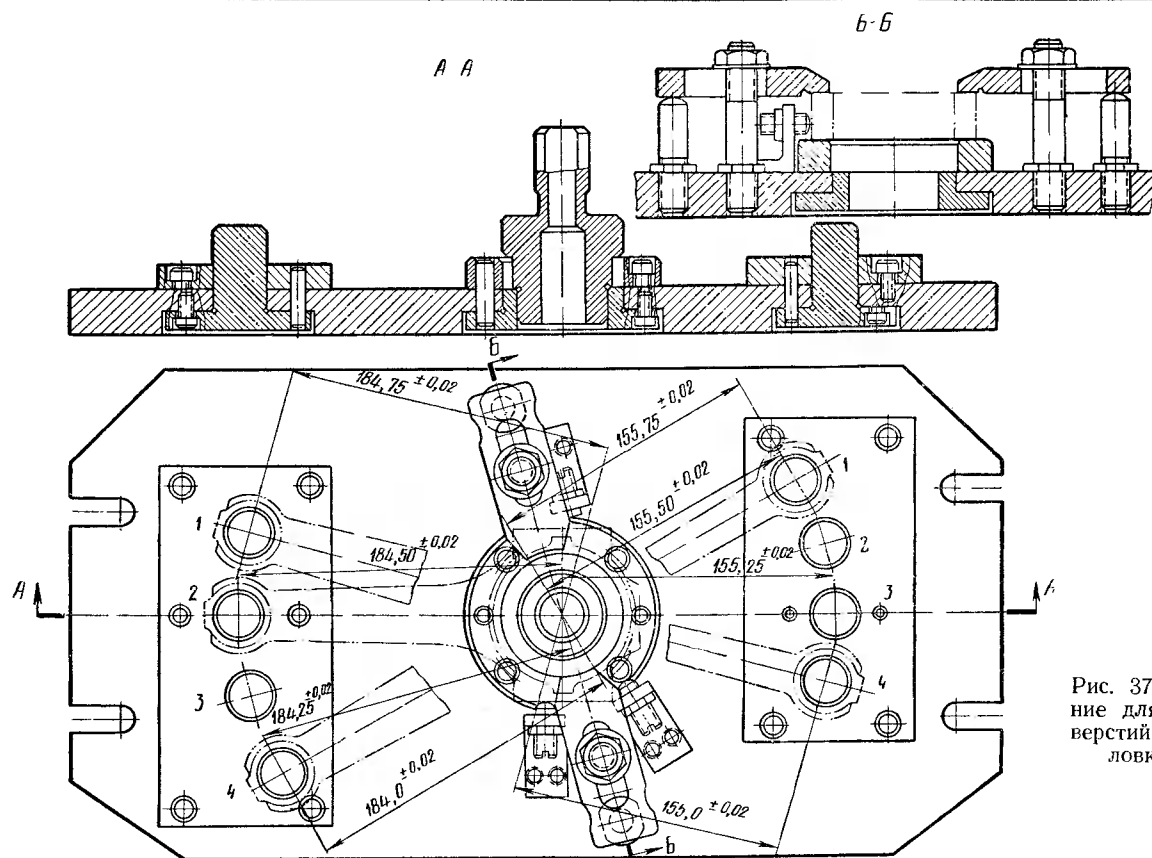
Приспособление для расточки отверстий в нижней головке шатунов
